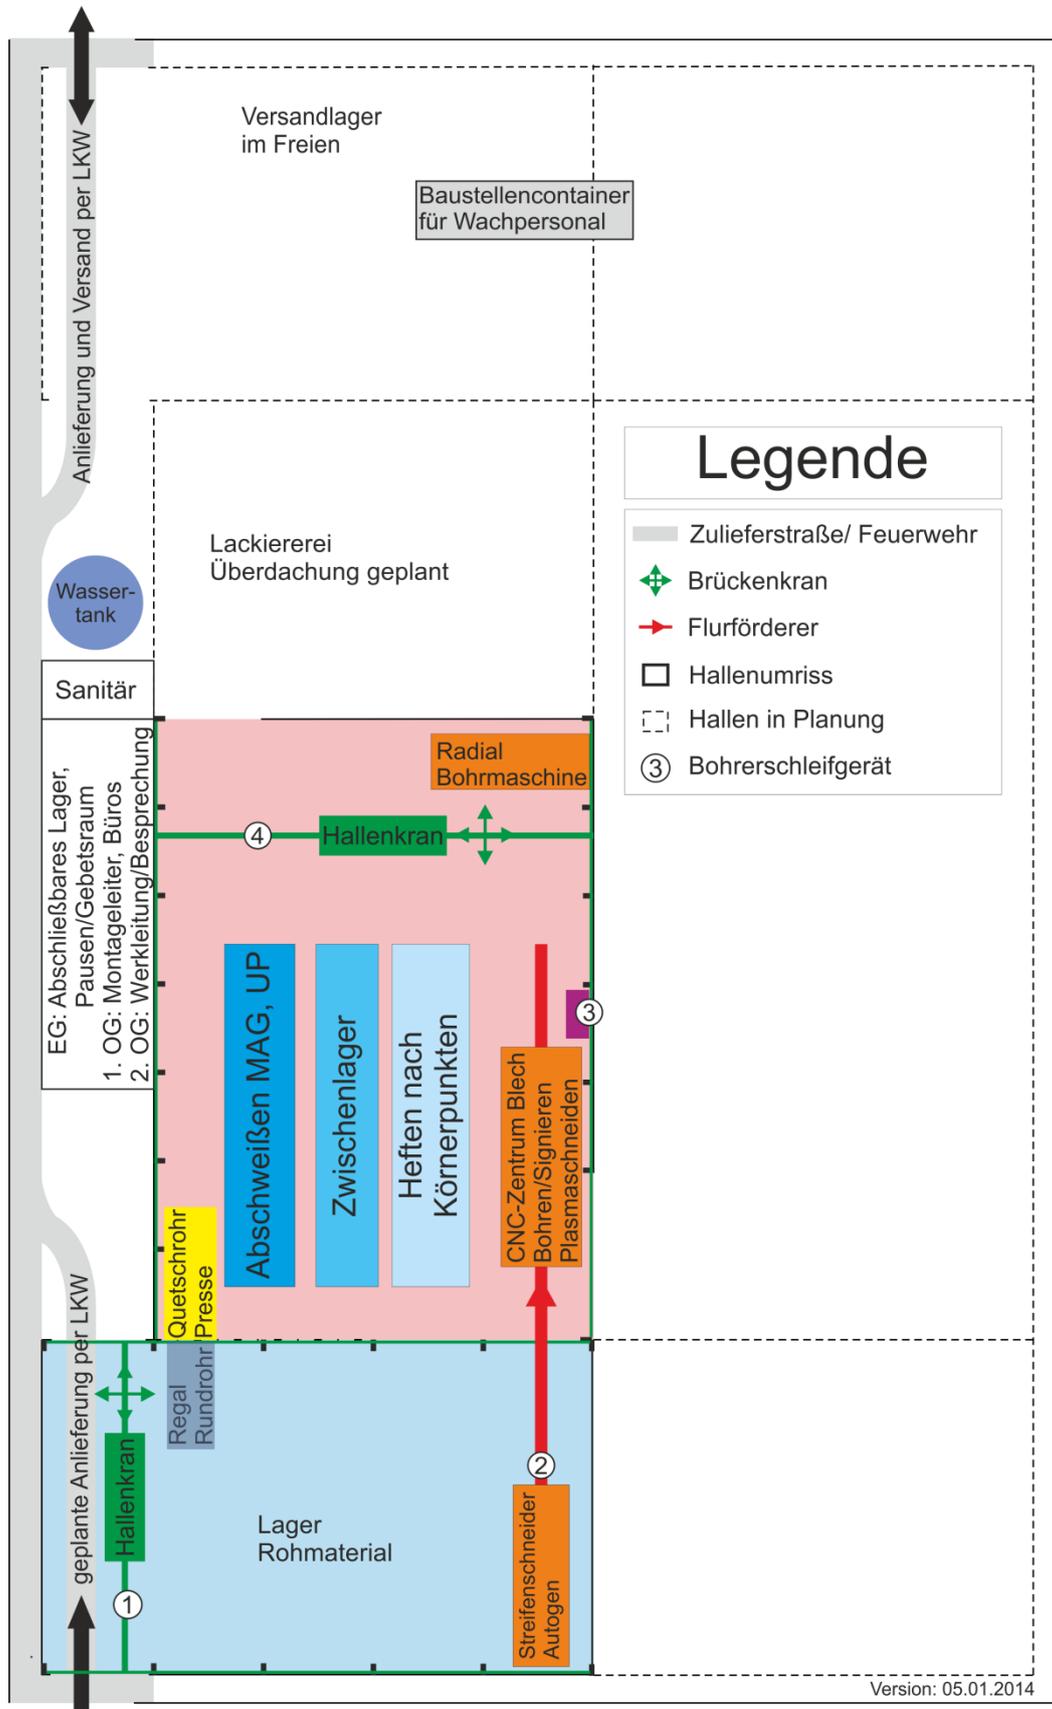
Werks- und Maschinenlayout, Muster für Entwicklungsländer
